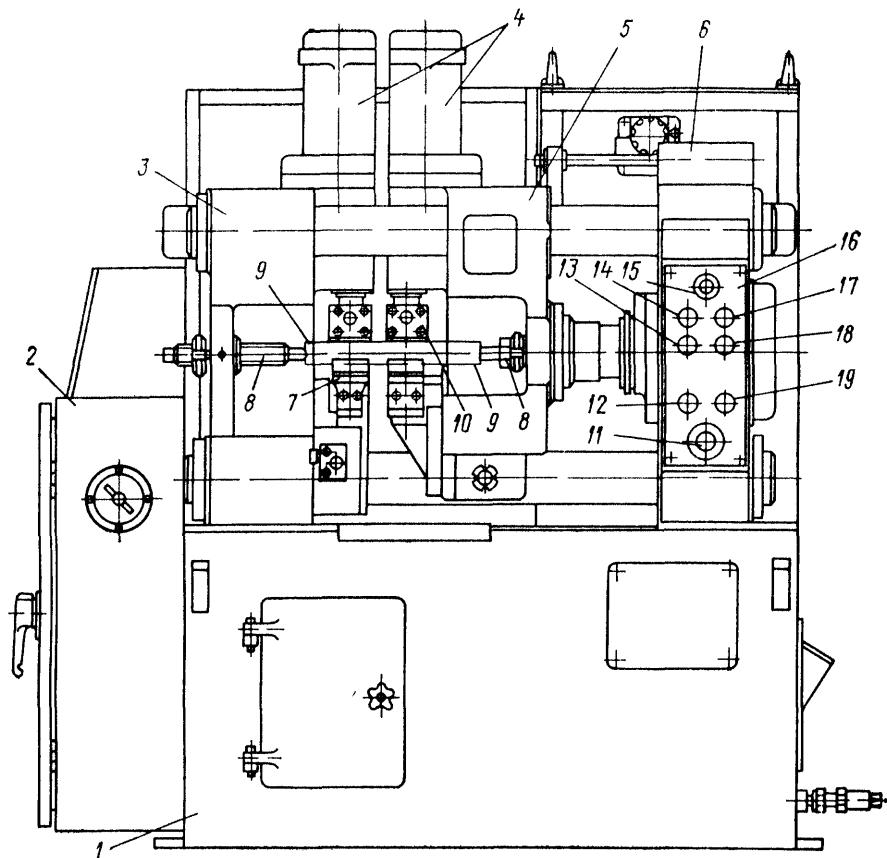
Сварочный полуавтомат модели СА-2:
